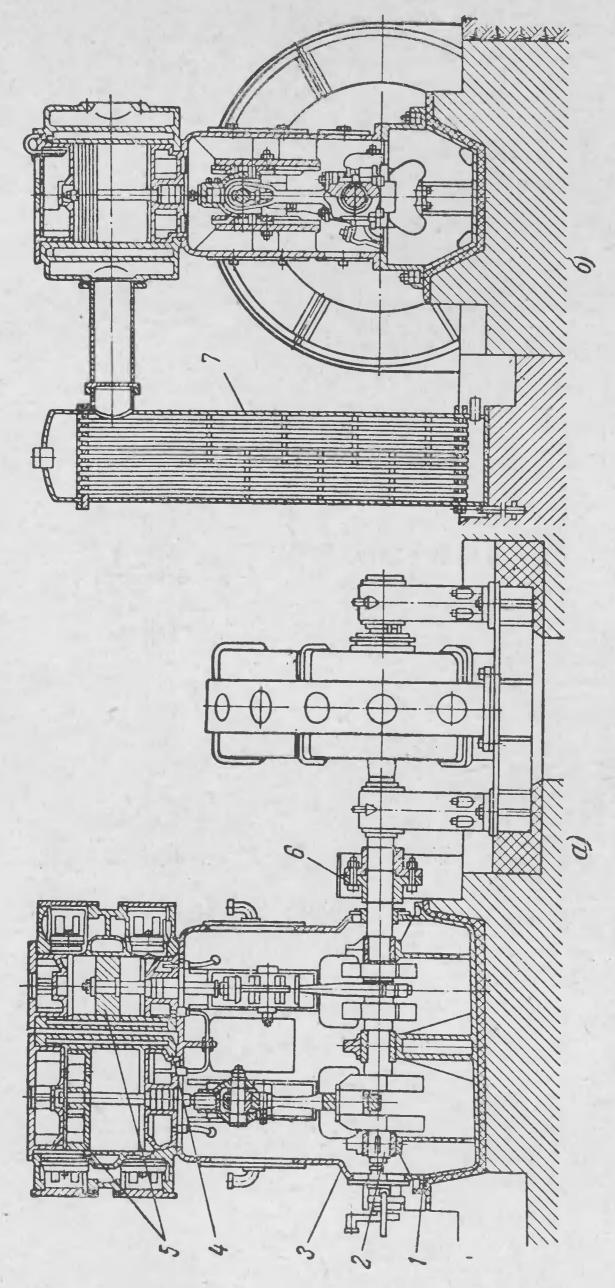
Компрессор В-300-2К (воздушный, ход поршня 300 мм, двухступенчатый, крейцкопфный). а-продольный разрез; 6-поперечный разрез.
